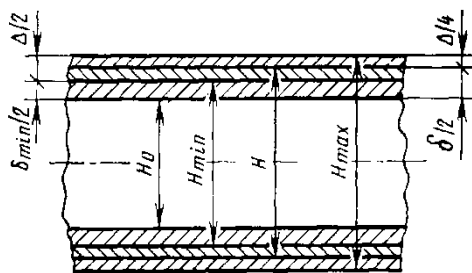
Схема расположения припусков и допусков на наружный размер детали, получаемой из поковки
